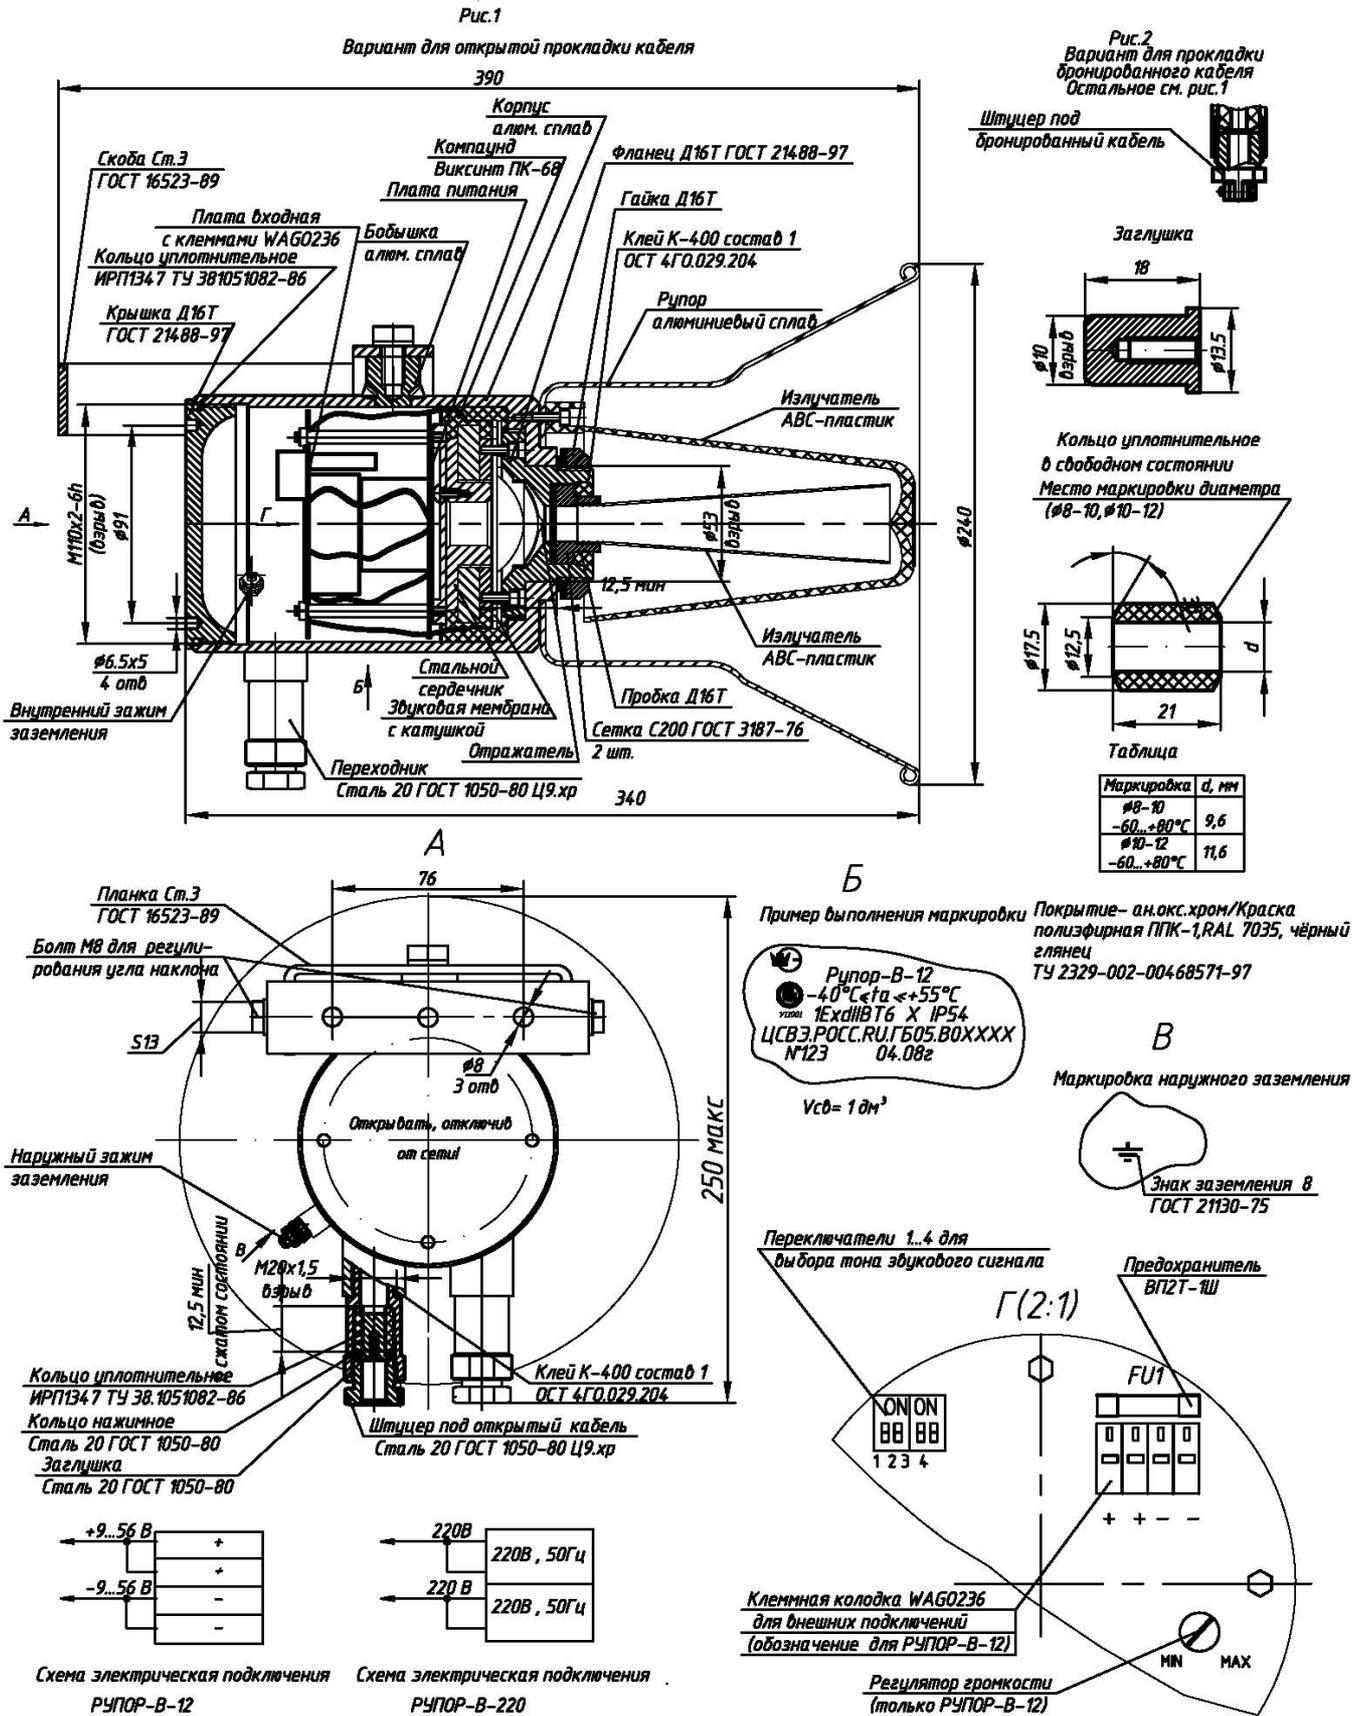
Габаритные размеры Оповещателя РУПОР-В с элементами взрывозащиты
